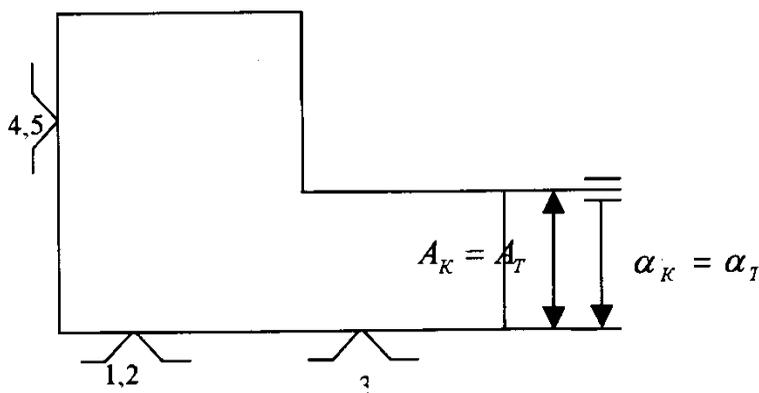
Схема базирования заготовки при получении линейного размера  $A_K$
